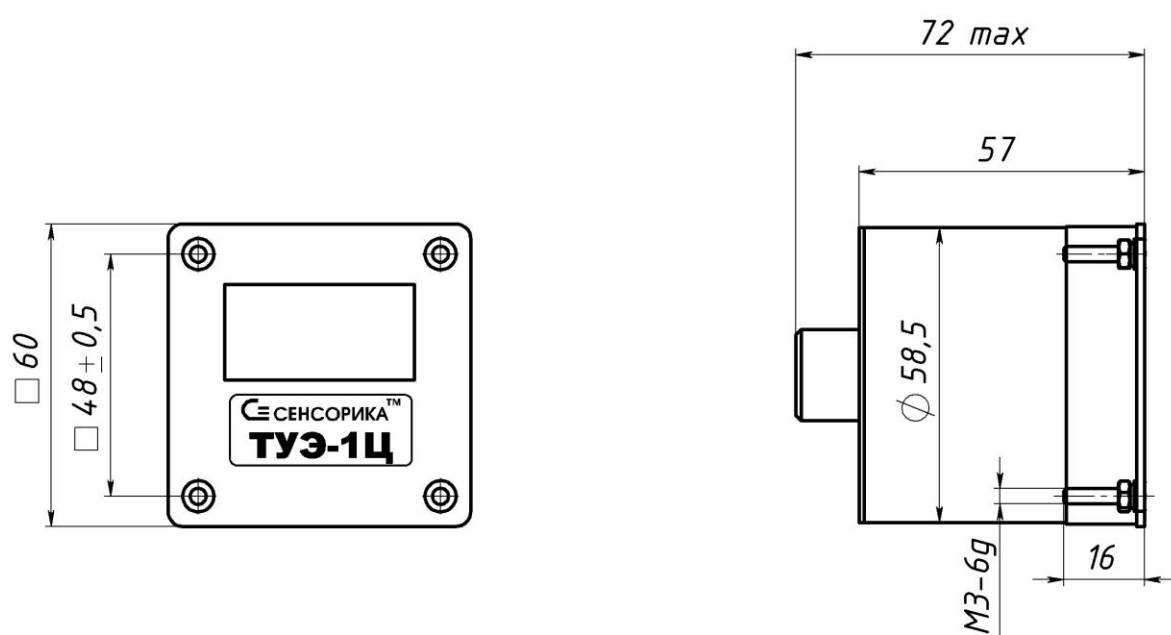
Габаритные размеры ТУЭ-1Ц
